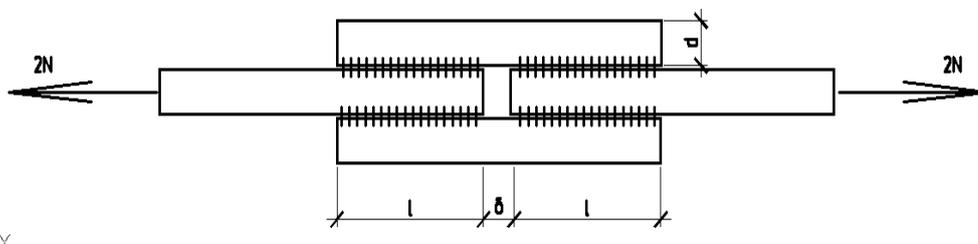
Конструктивная схема сварного стыкового соединения выполненного при помощи боковых накладок
